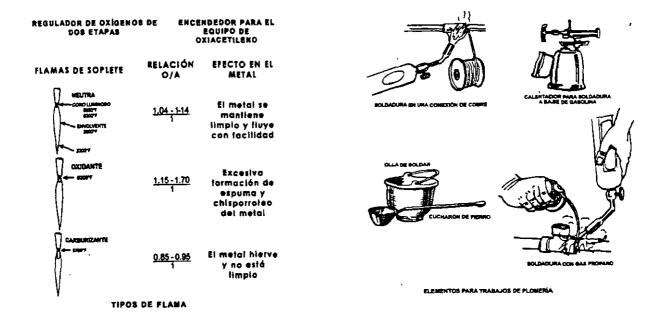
Accesorios y características de la soldadura con oxiacetileno.
